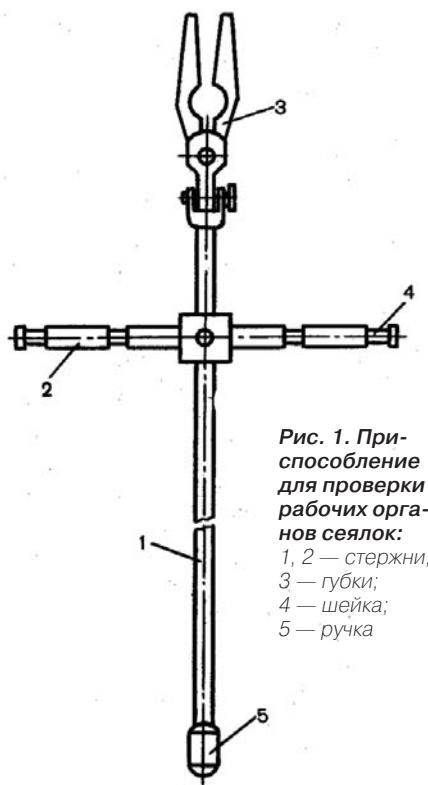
Приспособление для проверки рабочих органов сеялок:
